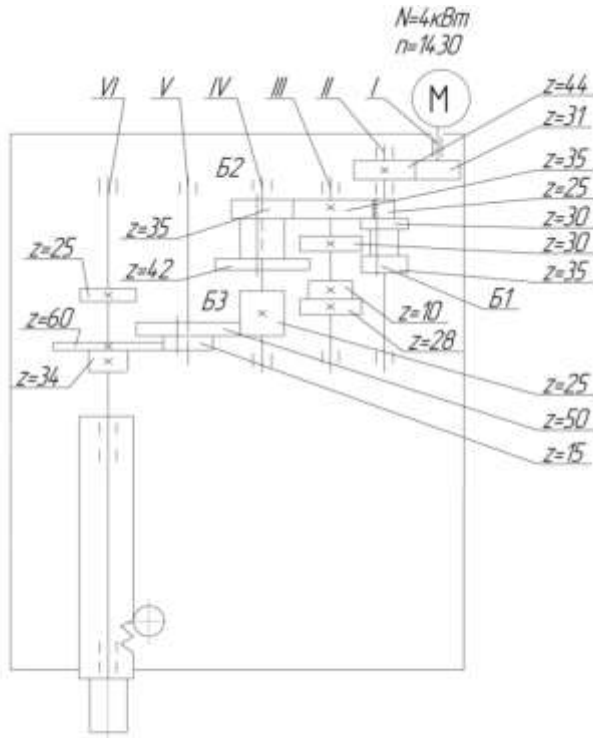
Кінематична схема коробки швидкостей вертикально-свердлильного верстата 2С132
